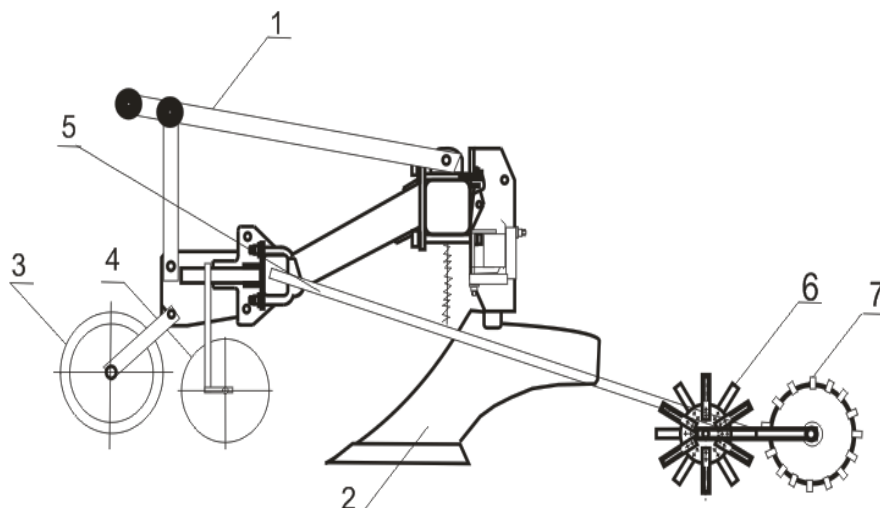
Компоновочная схема комбинированного почвообрабатывающего агрегата для подготовки почвы под посев бахчевых культур: 1 - рама; 2 - право – и левооборачивающие плужные корпуса; 3 - опорное колесо; 4 - дисковый нож; 5 – тяга; 6 – батарея дисков с разнонаправленными сферическими ножевыми элементами; 7 - планчатые катки
